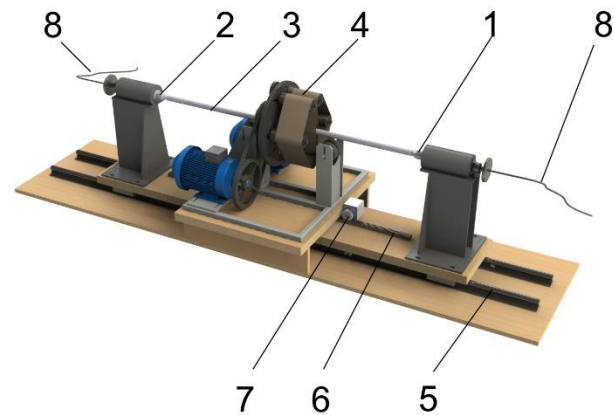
Схема установки для измерения сил резания: 1, 2 — передний и задний тензометрические центра соответственно; 3 — заготовка; 4 — установка для ротационного ленточного шлифования; 5 — направляющие станины; 6 — зубчатая рейка; 7 — шаговый электродвигатель; 8 — провода, ведущие к прибору для измерения сил резания
